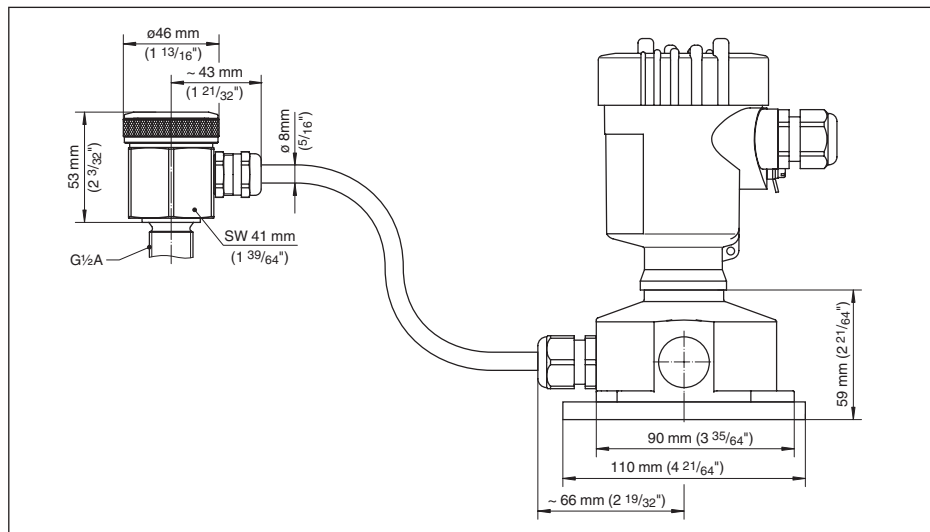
Корпус датчика - IP 67 и выносной корпус прибора
